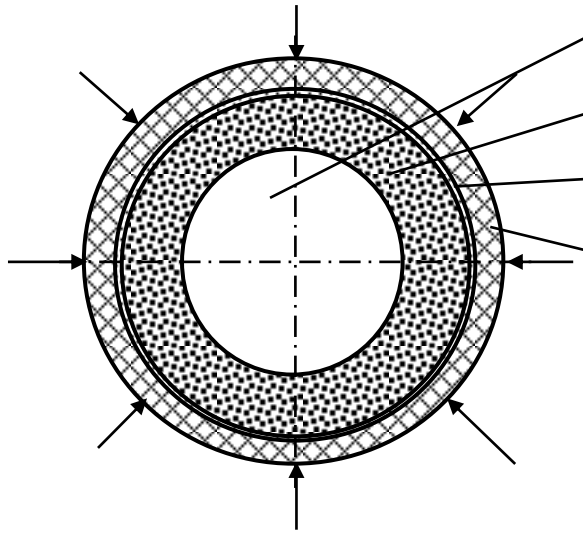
Схема виготовлення керамічного шару фільтруючого матеріалу: 1 – оправка; 2 – керамічний шар; 3 – прошарок; 4 – оболонка
